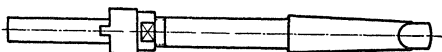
Dorn für Aufsteckreibahlen mit kegelförmigem Schaft.
